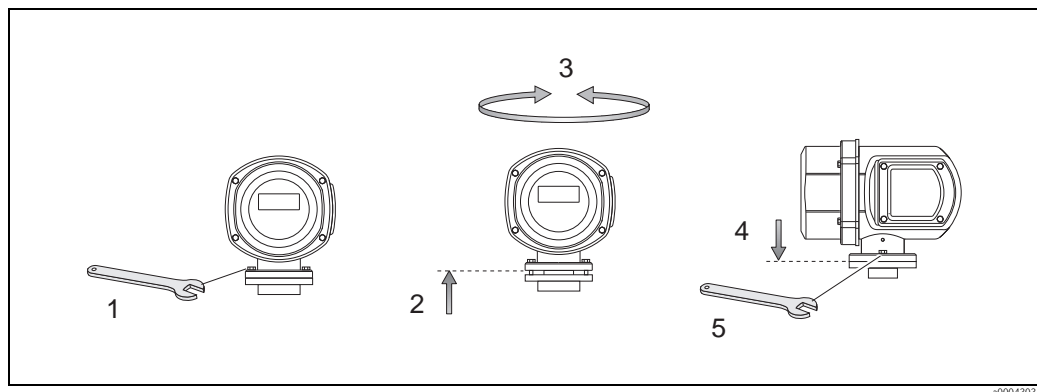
Drehen des Messumformergehäuses (Edelstahl-Feldgehäuse)
